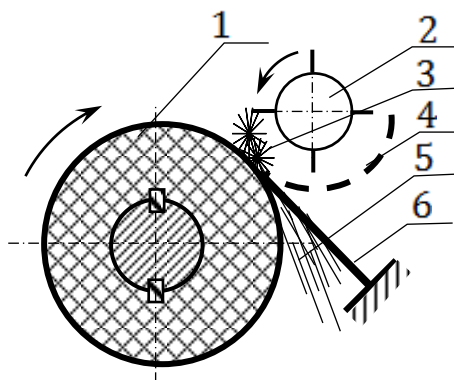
Основные рабочие органы валичного джина марки ДВ – 1М: 1 - джинурующий барабан; 2 - отбойный барабан; 3 - летучка хлопка-сырца; 4- перфорированная сетка; 5 - холст волокна; 6 - неподвижный нож.
